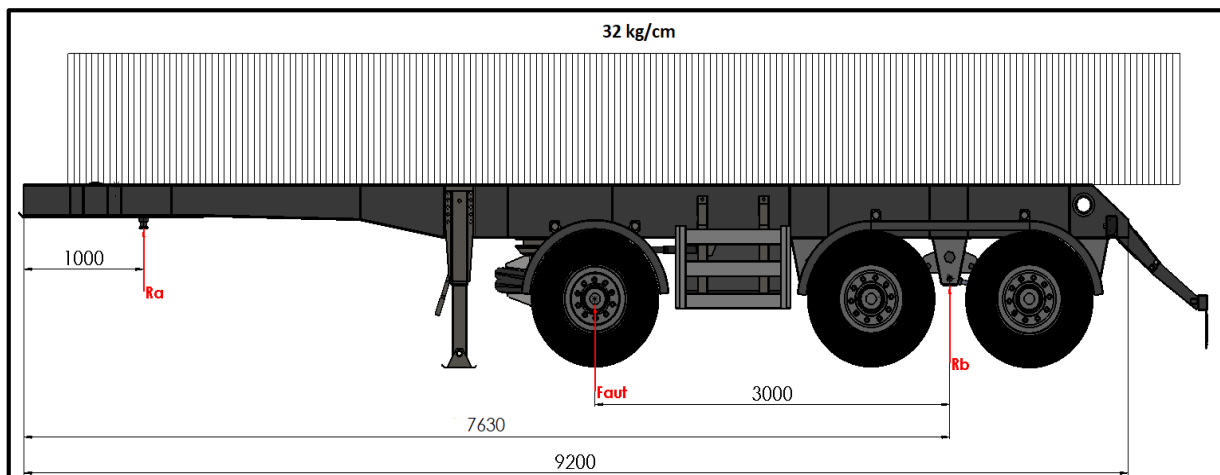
Viga con eje levadizo trabajando y con cargas de impacto
